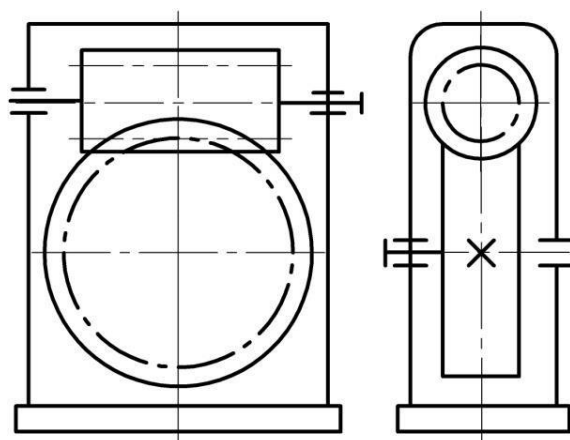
Червячный редуктор с верхним расположением червяка
